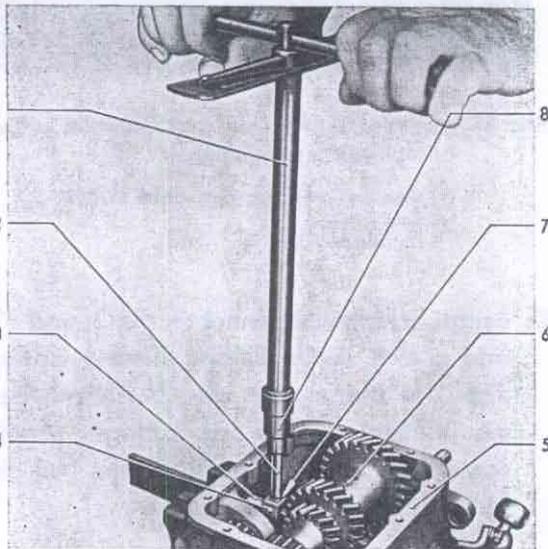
Zwischenhebel auf Getriebeschaltwelle befestigen
